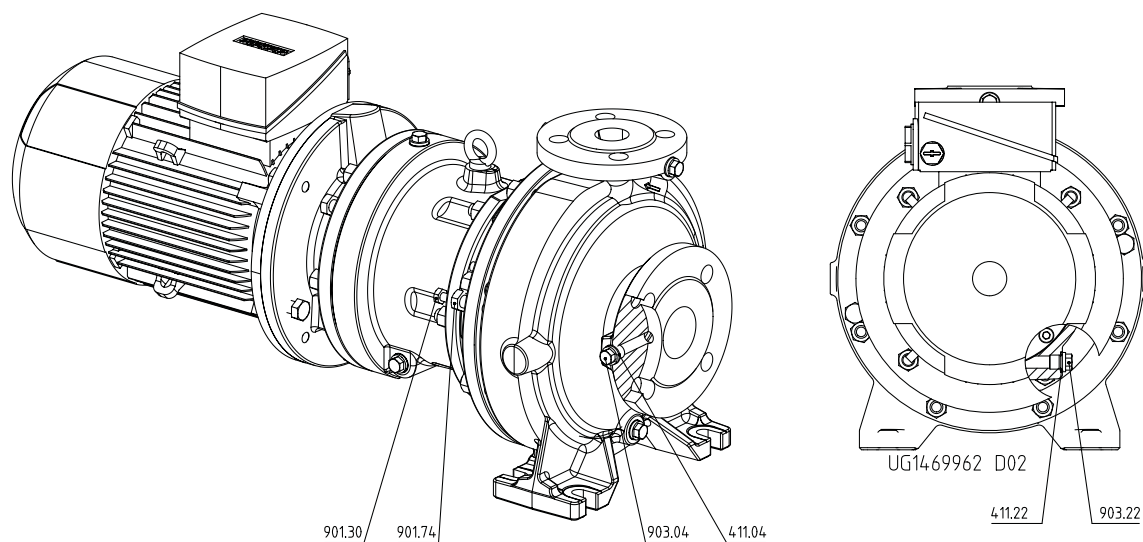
Befestigung Druckdeckel am Pumpengehäuse bei Ausführung mit geschraubtem Deckel
